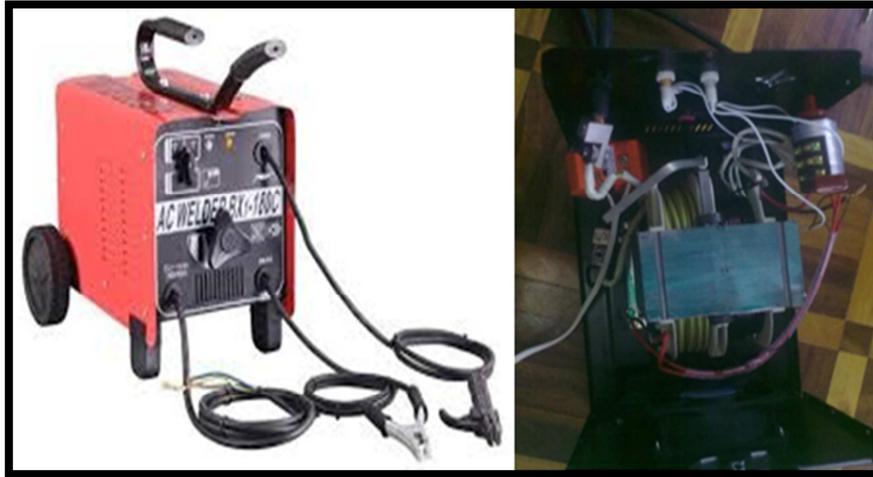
SOLDADORA AC WELDER BX1- 32 50 CK
